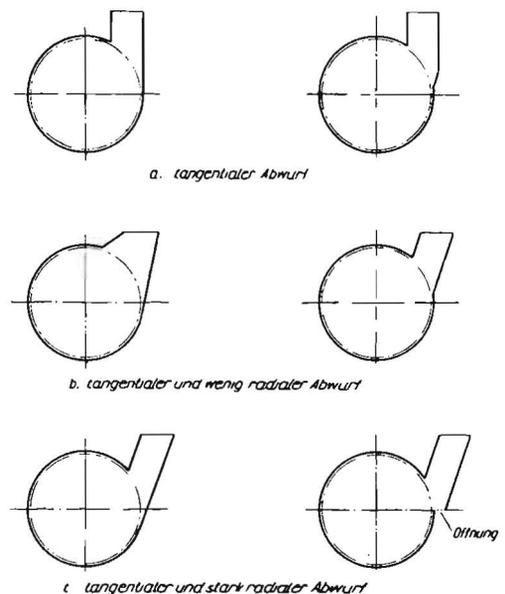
Gehäuseausführungen bei Wurfgebläsen (links alte, rechts verbesserte Ausführung)
